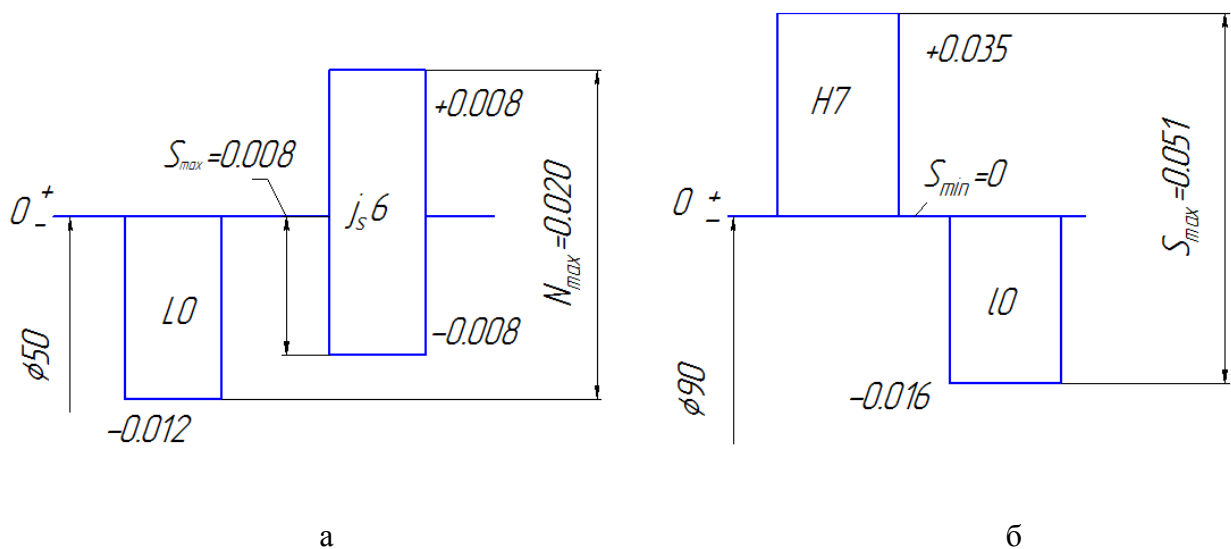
Схеми розташування полів допусків підшипникових посадок: а - внутрішнього кільця підшипника з валом; б - зовнішнього кільця підшипника з отвором корпусу
